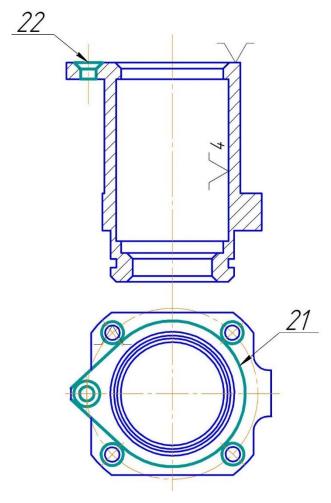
Эскиз для фрезерной операции с ЧПУ
